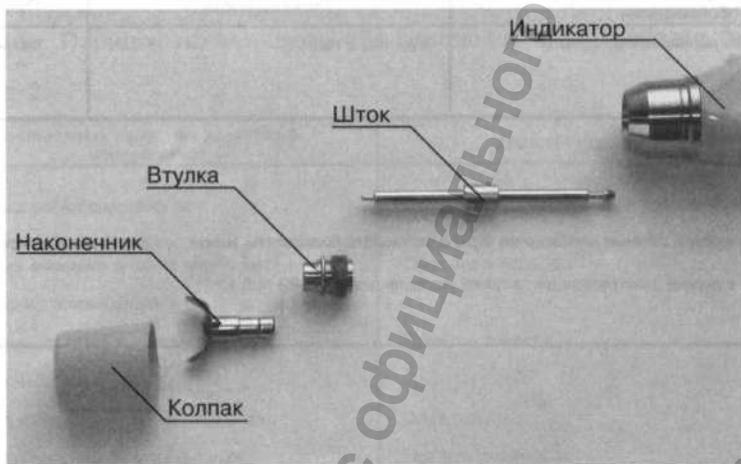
Подготовка индикатора к очистке штокового механизма
